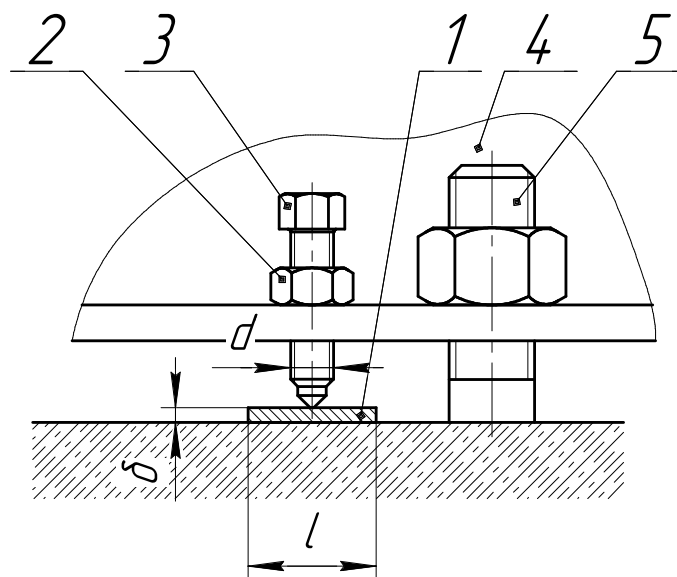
Схема выверки отжимными регулировочными винтами:
